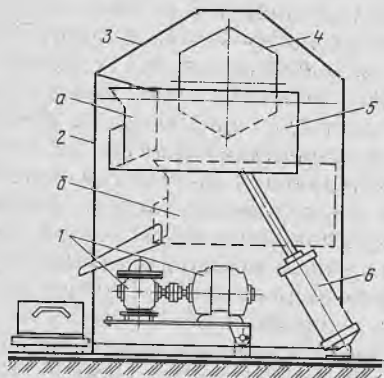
Установка для мойки мелких деталей во вращающемся барабане:
